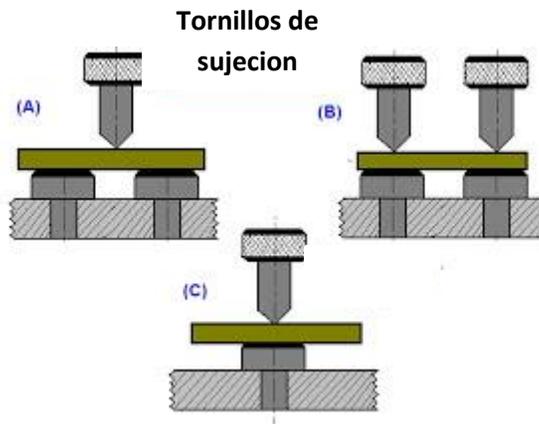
Tornillos de sujeción. Fuente: American Machinist
